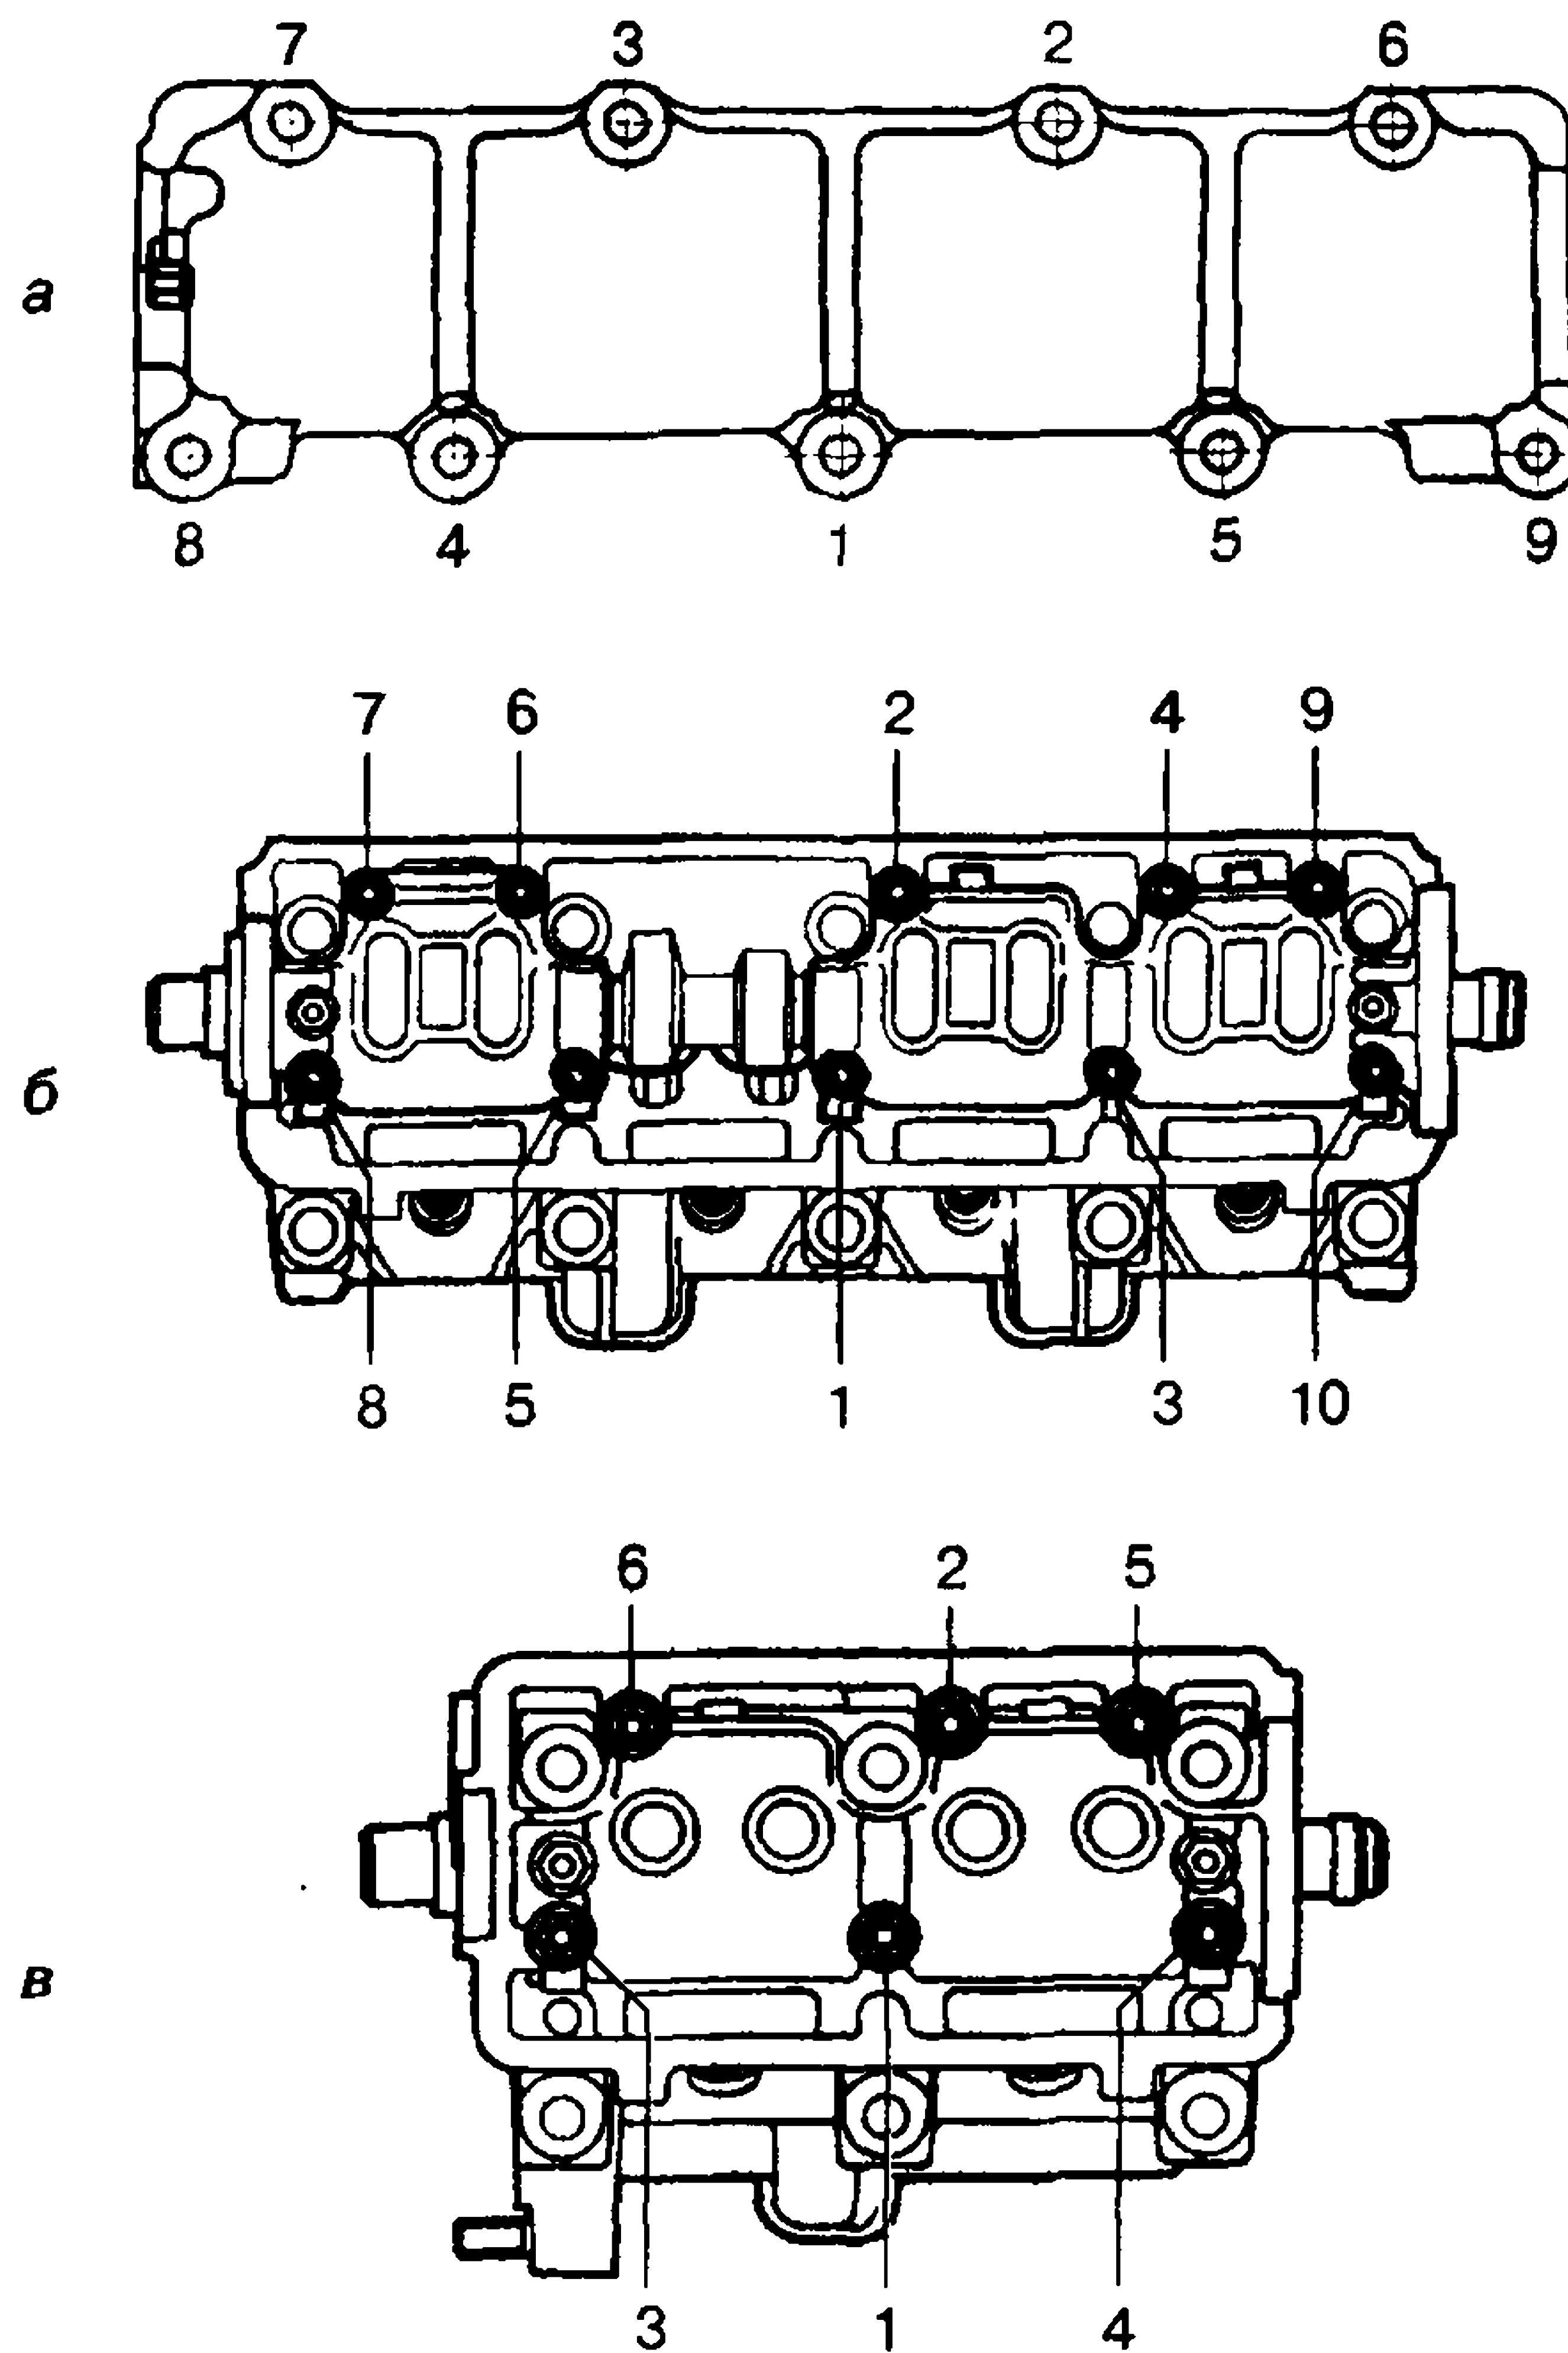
Последовательность затяжки гаек крепления корпусов подшипников распределительного вала:
